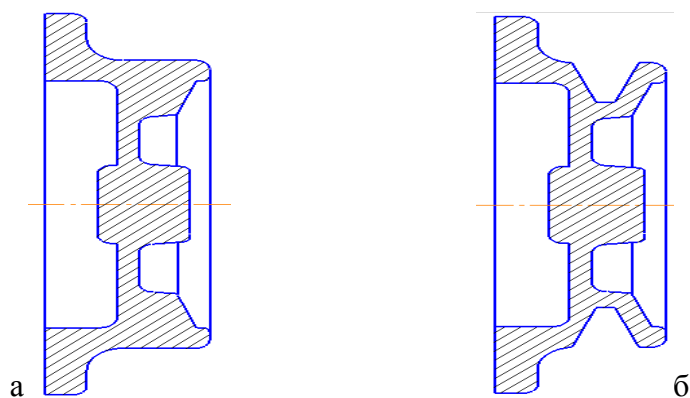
Общий вид отливки шкива 260-1307124, материал - серый чугун, изделие ОАО «БЗА». а – первоначальный, б – предлагаемый
